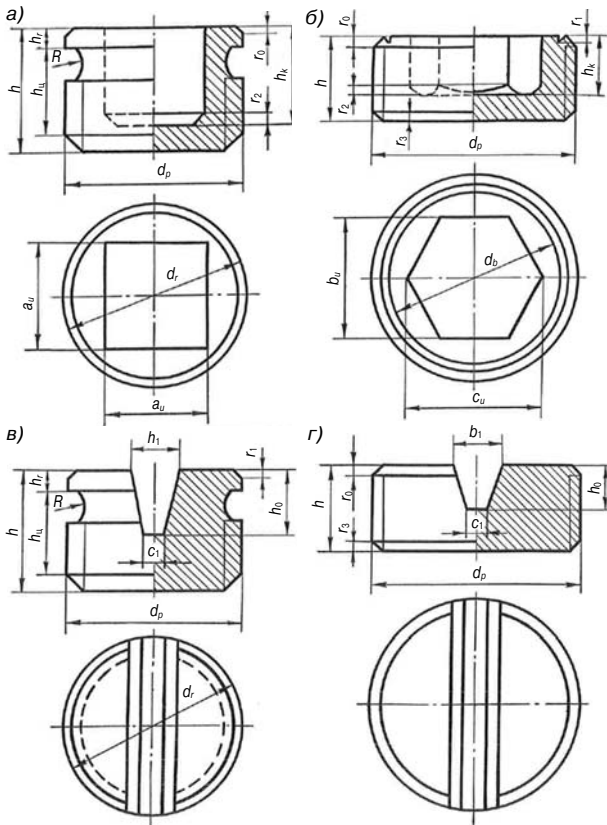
Конструкция пробок грязесборника в шатунных шейках коленчатого вала двигателей: а, б — существующие; в, г — разработанные для двигателей рабочими объемами 4,25 (в), 6 и 7 л (г)
